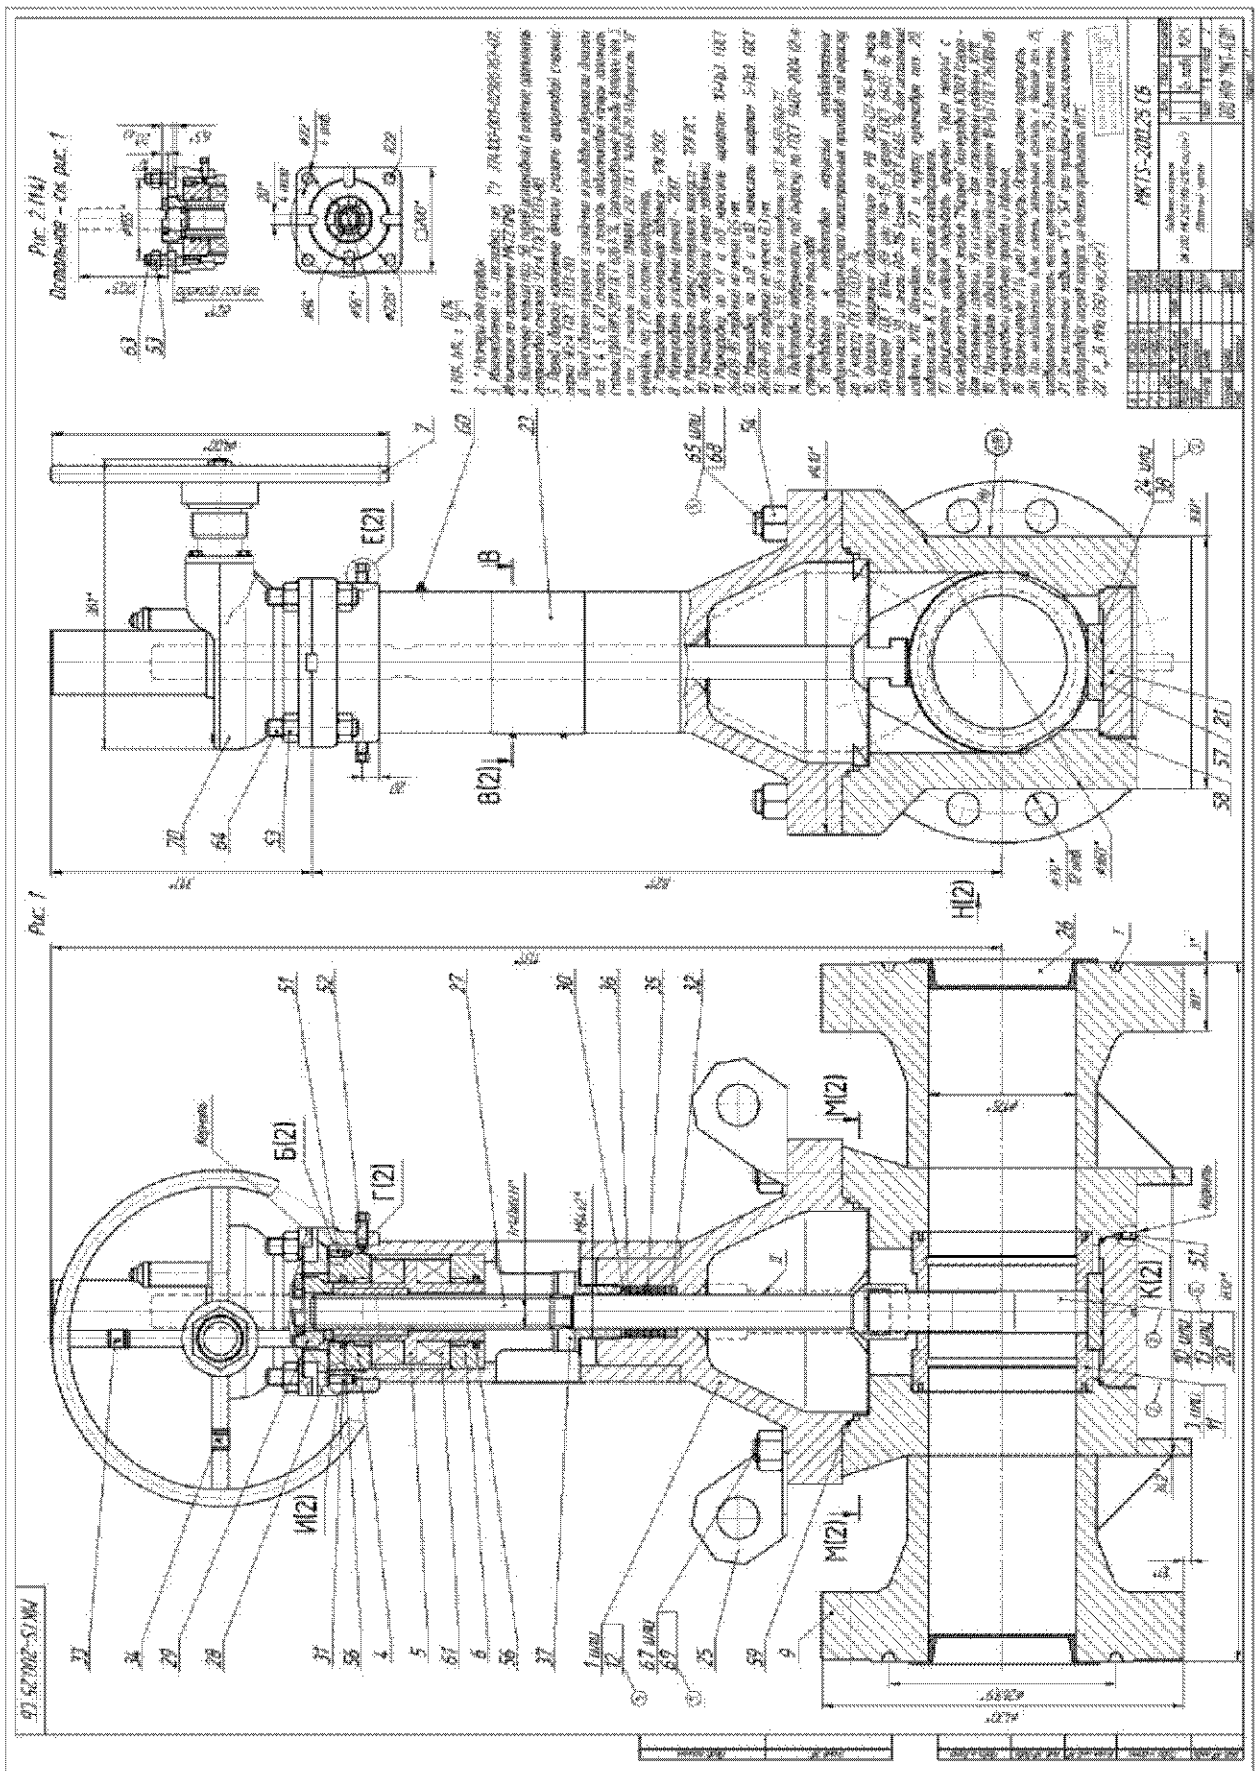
Сборочный чертеж узла «Задвижка запорная»
